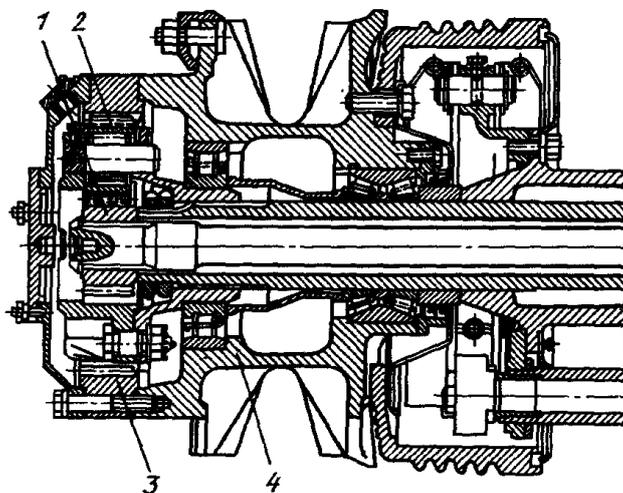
Разнесенная главная передача с колесными редукторами
